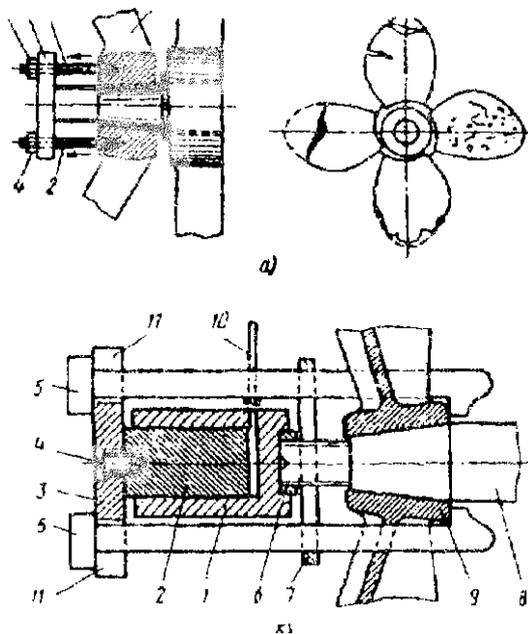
Снятие винта с гребного вала: а - при помощи болтов: 1 - винт; 2 - болт; 3 - планка; 4 - гайка. б - гидравлическим прессом: 1 - корпус пресса; 2 - плунжер; 3 - сменная опорная плита; 4 - винт крепления; 5 - тяговые рычаги; в - сменное установочное кольцо; 7 - кольцо для стяжки рычагов; 8 - гребной вал; 9 - ступица гребного винта; 10 трубка; 11 - пазы опорной плиты.
